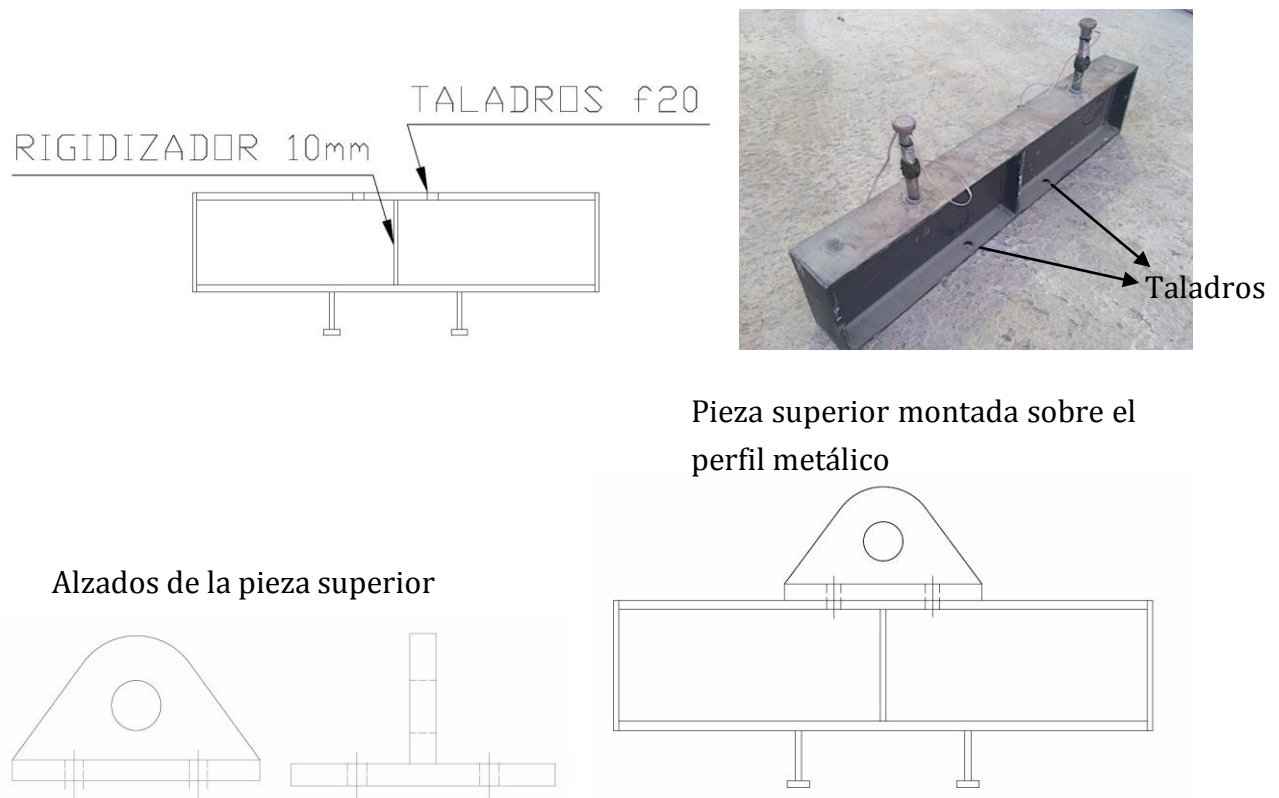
Taladros, rigidizador y pieza superior del perfil metálico.
